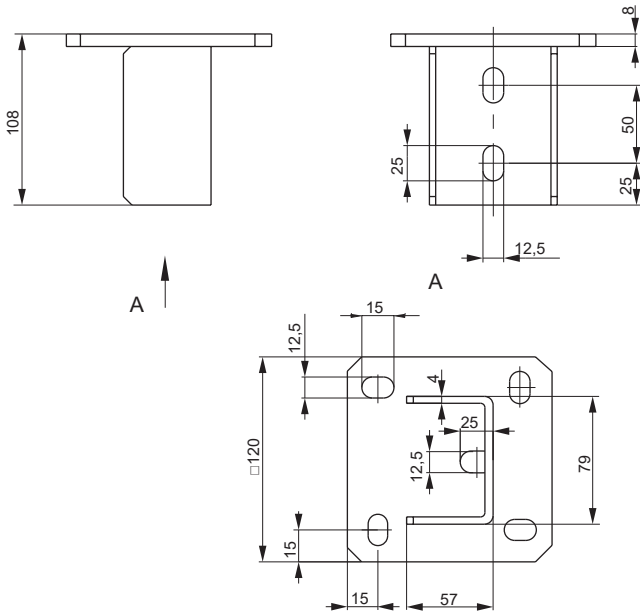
Крепление потолочное усиленное / Figure B.3 – Reinforced ceiling attachment
